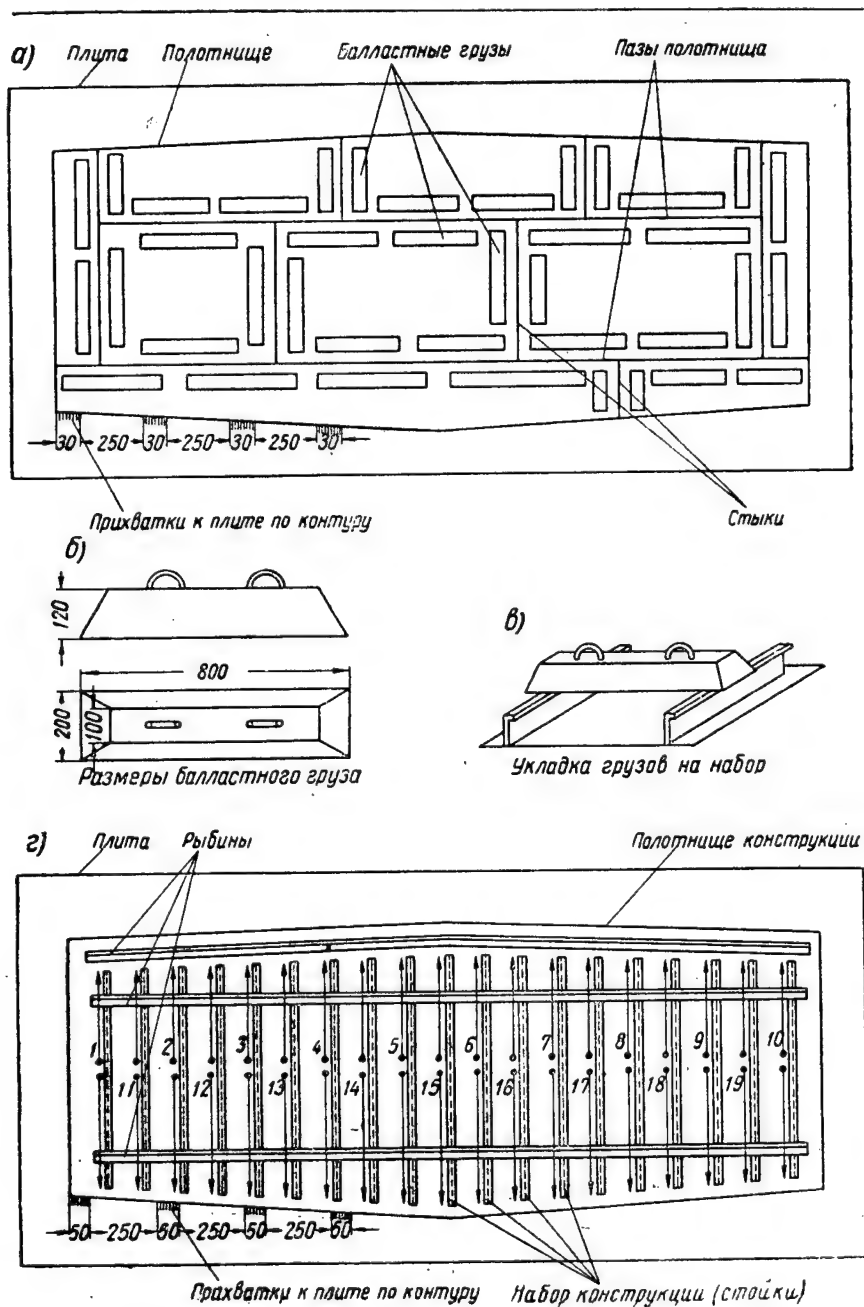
Сборка и сварка тонколистовых конструкций
